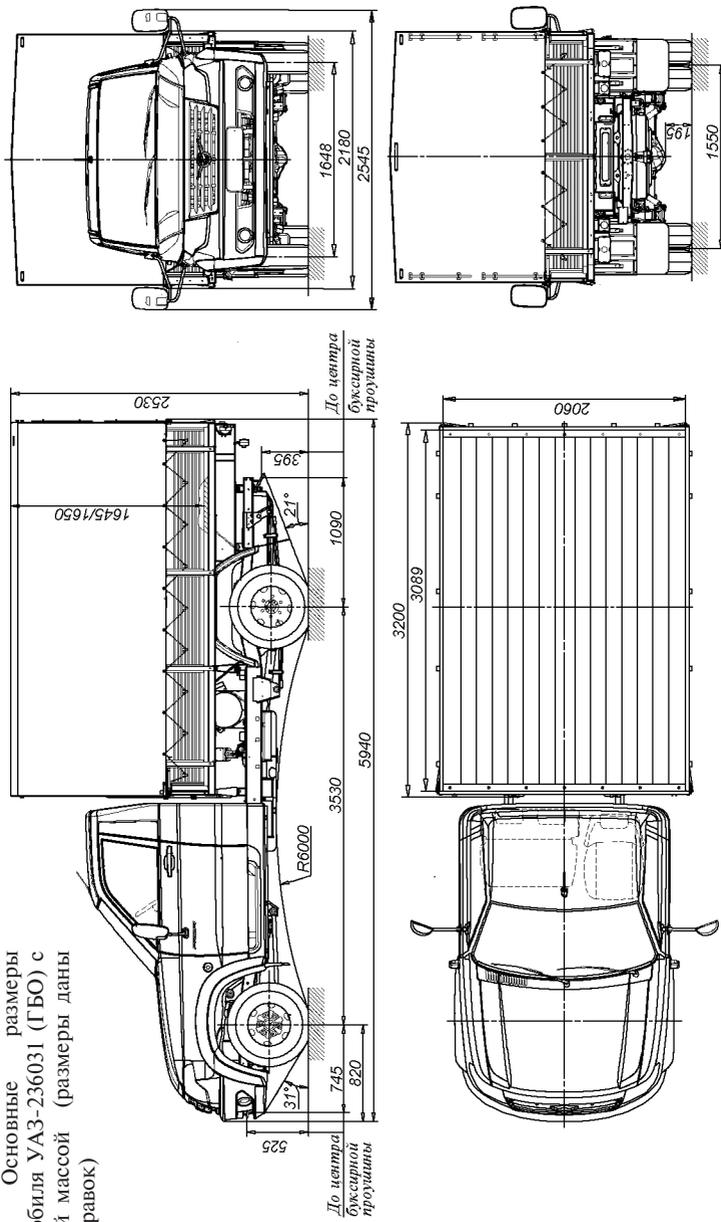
Основные размеры автомобиля УАЗ-236031 (ГБО) с полной массой (размеры даны для справок)
